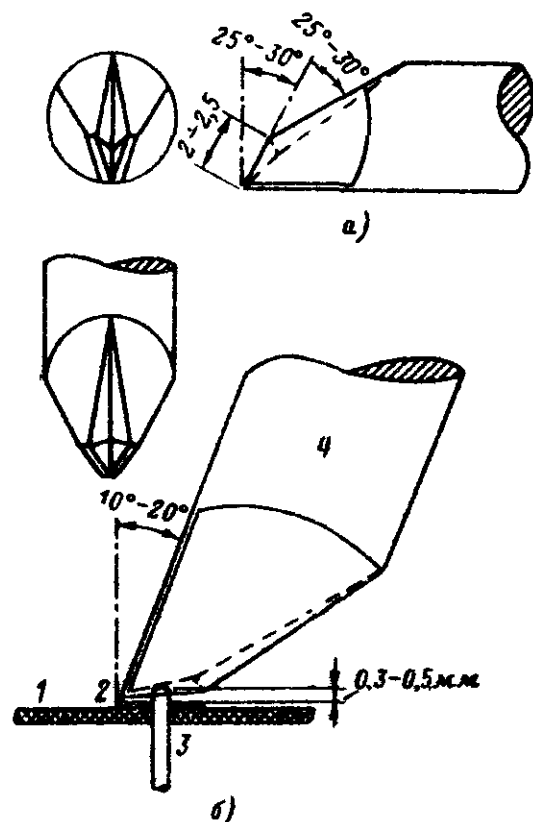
Форма жала паяльника. а — заточка жала; б — положение паяльника при пайке; 1 — печатная плата; 2 — контактная площадка; 3 — вывод детали; 4 — жало паяльника.
